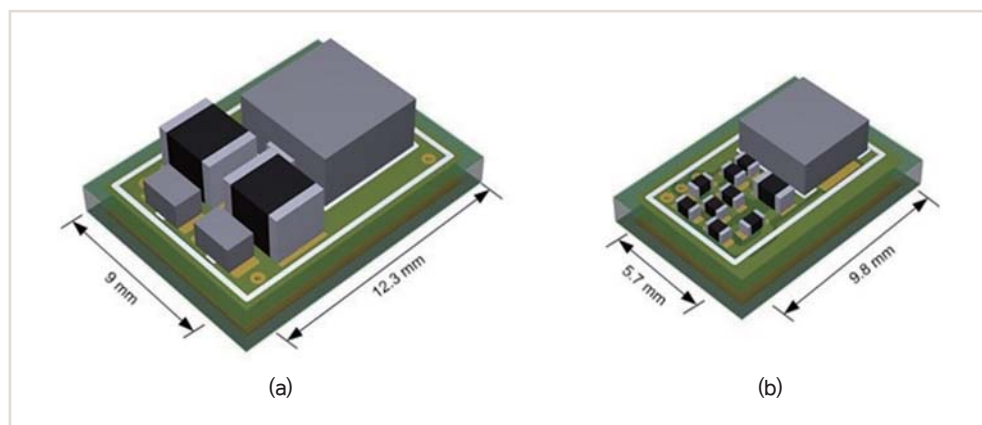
수동(a) 및 능동(b) 필터 설계의 PCB 레이아웃 크기 비교
